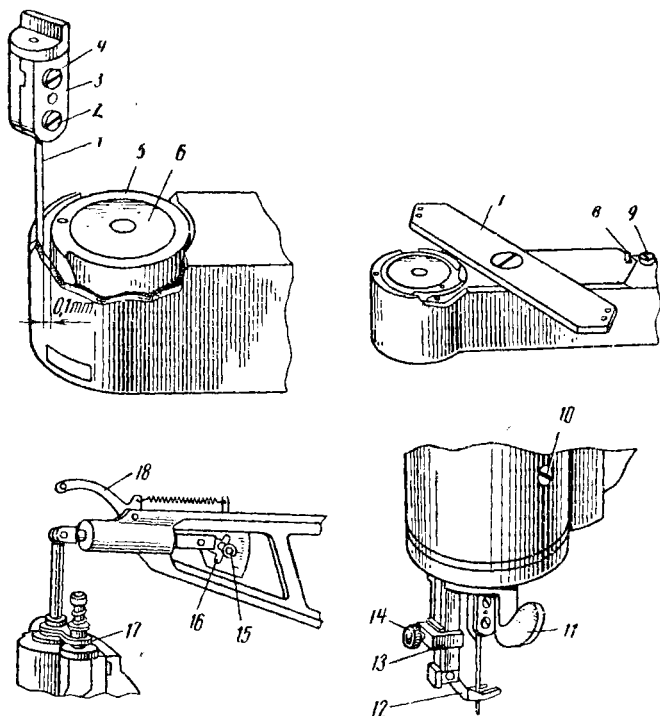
Исполнительные органы швейной машины для ремонта верха и подкладки:
